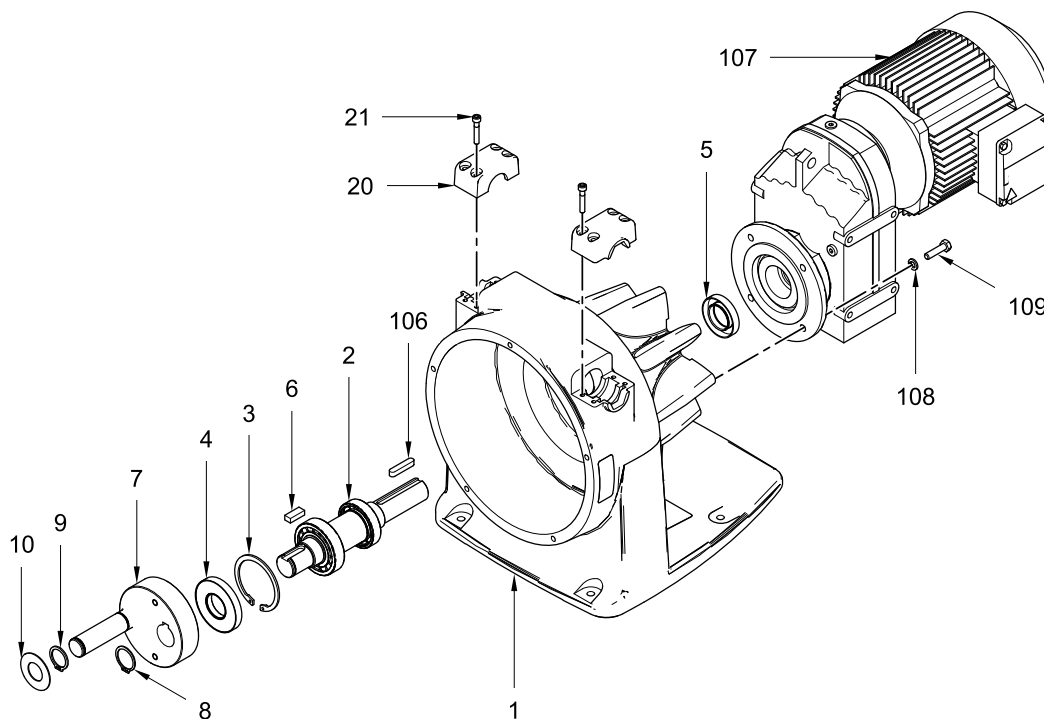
Удаление эксцентрикового и выходного вала двигателя
